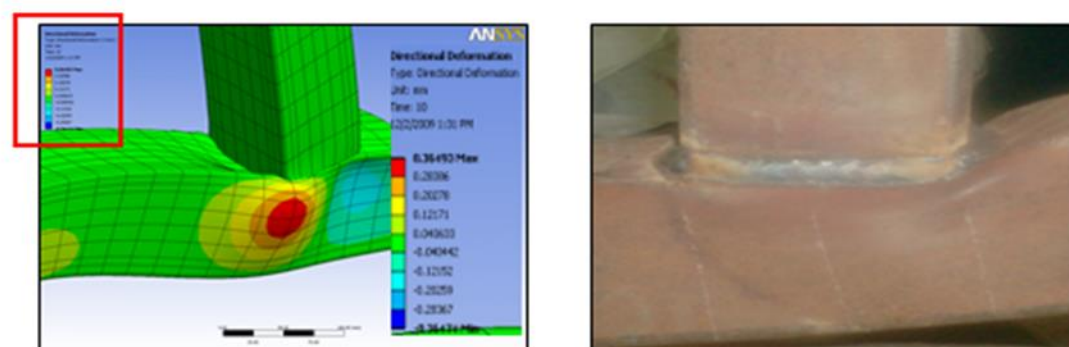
a) Distorsión teórica 20, b) Distorsión experimental ensanchamiento de la sección transversal de la columna del pórtico parámetro llamado (b_1) tubos de 90x90x2.50mm. Ensayo 3. Fuente: [8]
